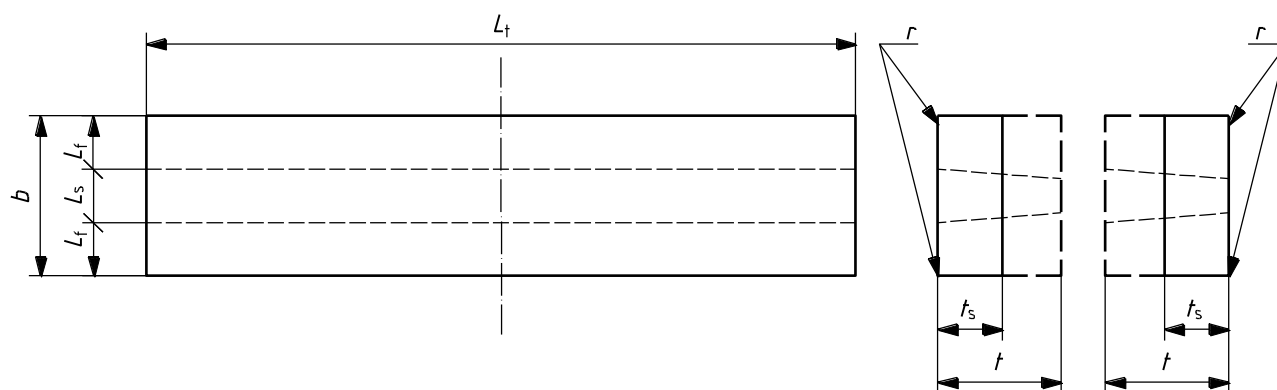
Продольный образец для испытаний на загиб стыковых сварных швов (LFBB и LRBB)
